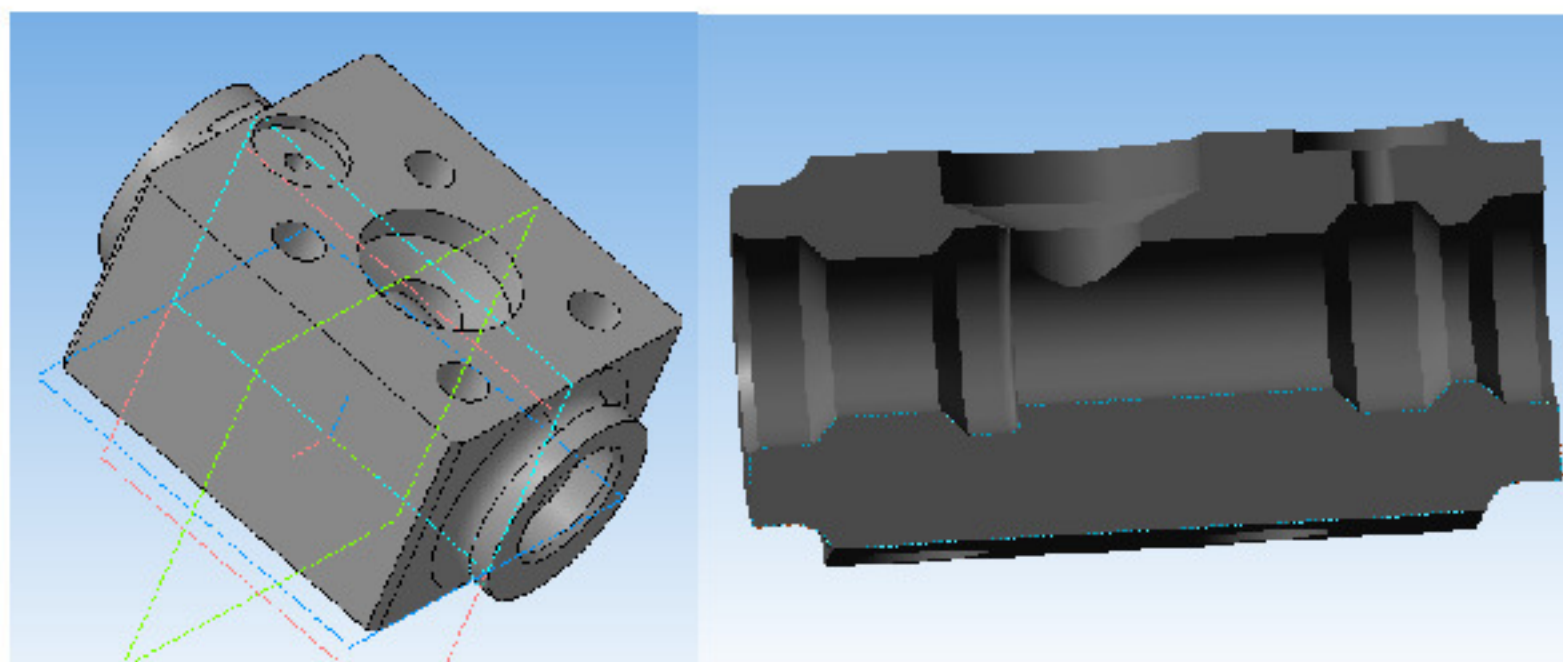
3D модель та розріз деталі «Корпус клапана КТ-48.001»
